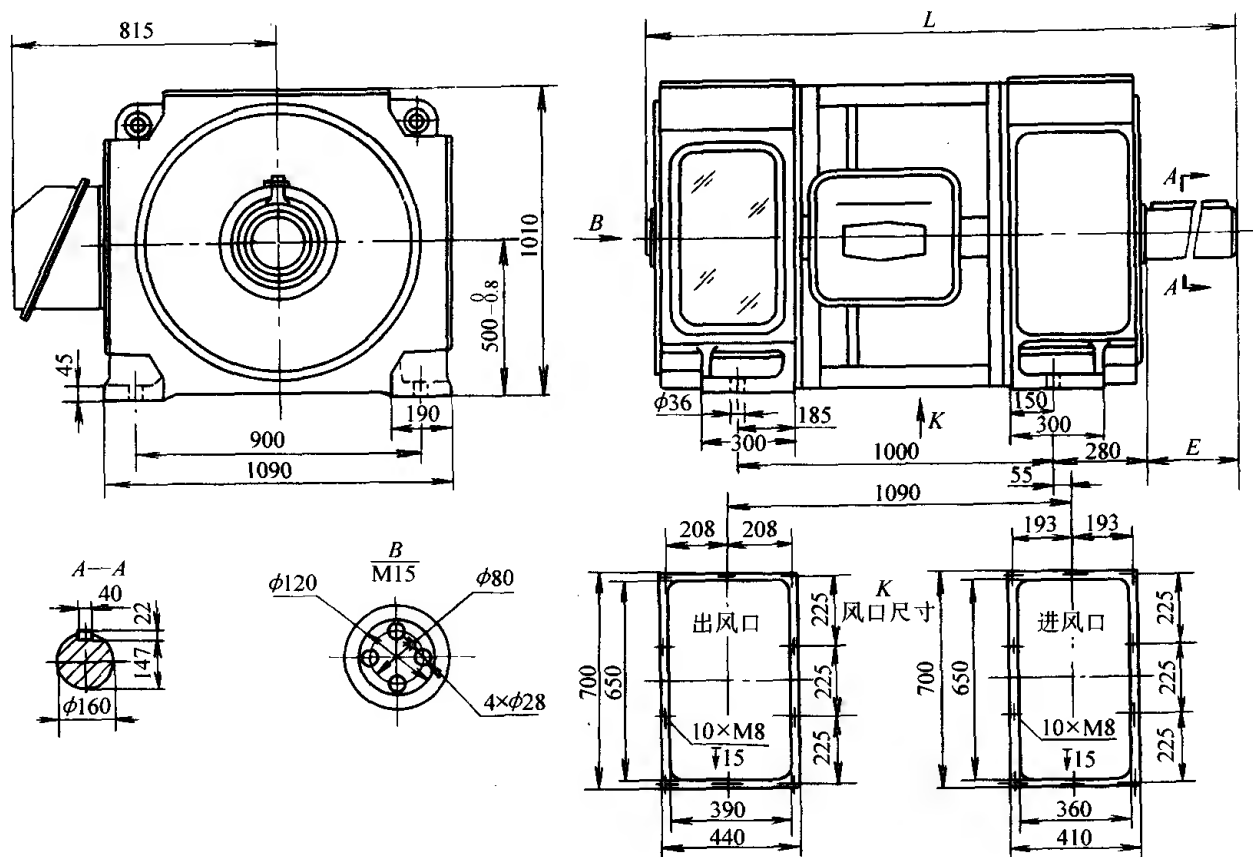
ZD3-500SIP 型 250kW 440V 320/1000r/min IC37 直流电动机安装及外形尺寸图
